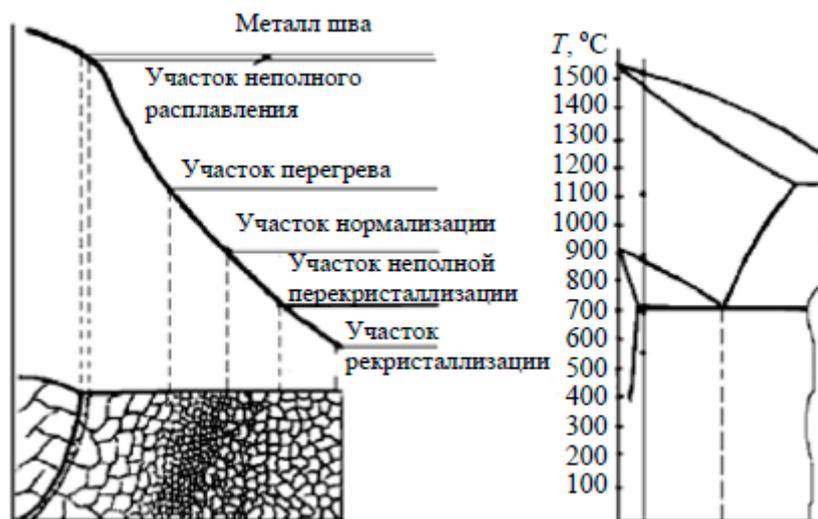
Строение ЗТВ при сварке низкоуглеродистой стали.
